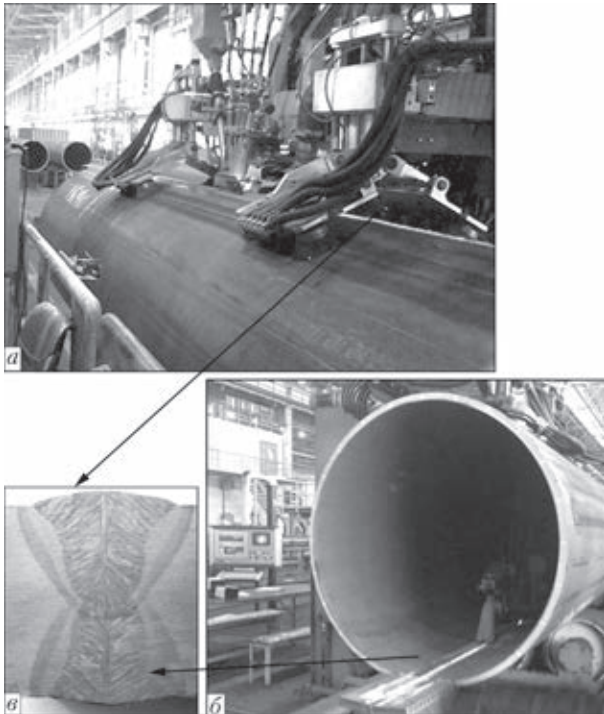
Многодуговая сварка под флюсом трубы диаметром 1420 мм с толщиной стенки 40 мм: *а* — 5-дуговая сварка наружного шва, скорость 110 м/ч; *б* — 4-дуговая сварка внутреннего шва, скорость 100 м/ч; *в* — макрошлиф сварного соединения трубы
